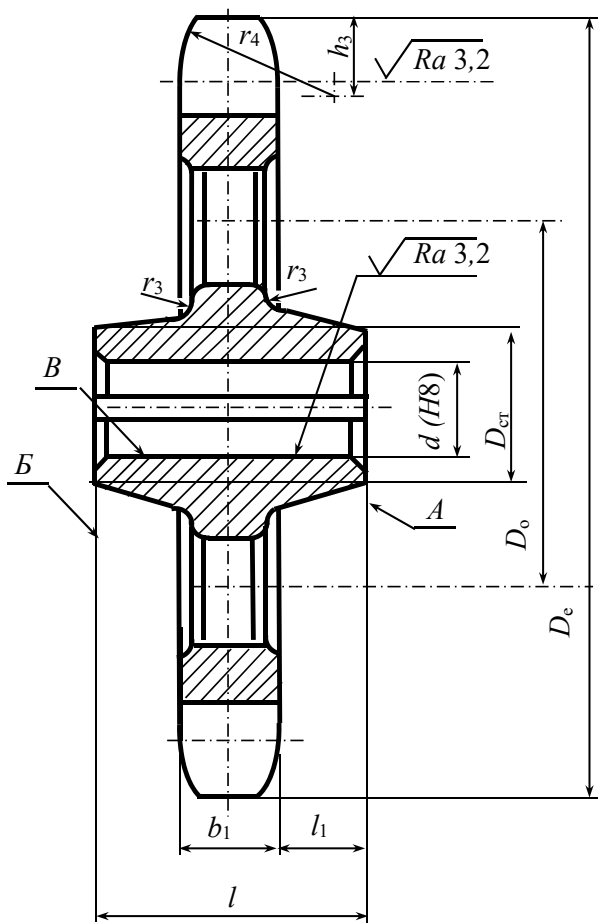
Эскиз звёздочки с большим числом зубьев
